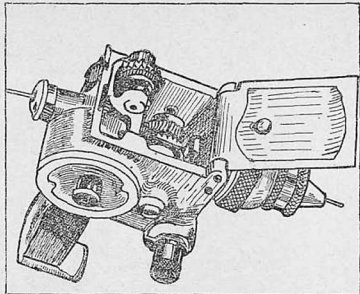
Металлоразбрызгиватель с открытой верхней крышкой
